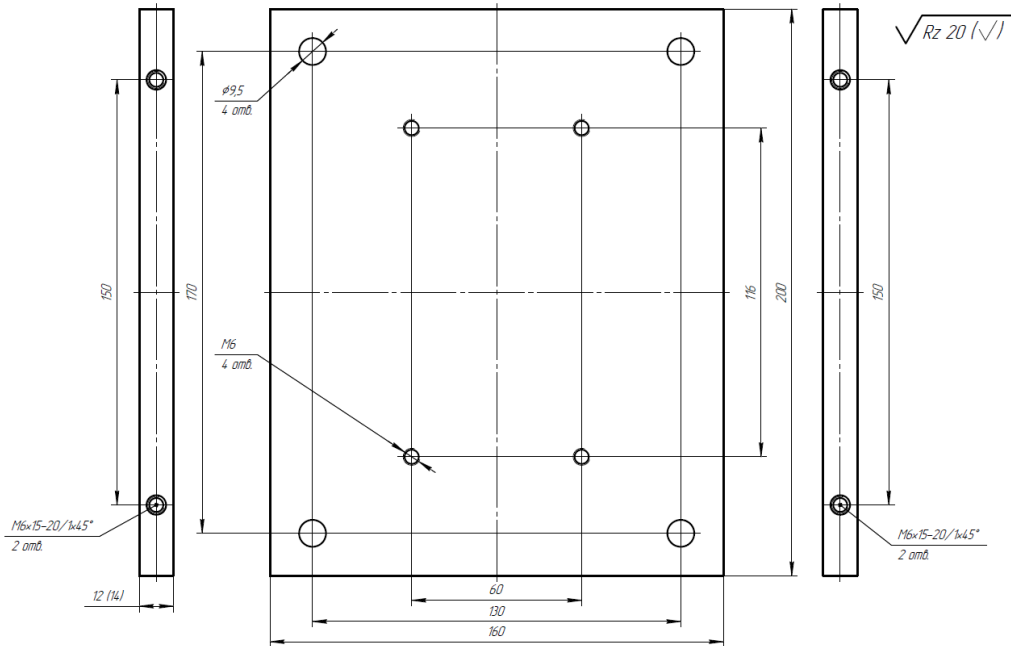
Чертеж монтажной пластины для установки инклинометра на бетонную поверхность
